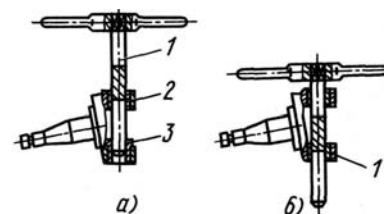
Развертывание втулок поворотного кулака: а — верхней втулки; б — нижней втулки; 1 — развертка; 2 — втулка биметаллическая; 3 — втулка направляющая
